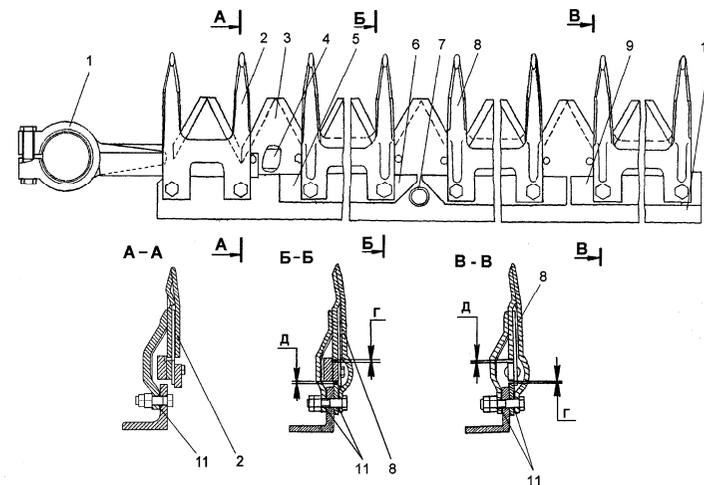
Режущий аппарат: 1 — головка ножа; 2, 8 — пальцы сдвоенные; 3 — сегмент; 4 — полоса ножевая; 5, 6, 9 — пластины трения; 7 — заглушка; 10 — уголок; 11 — прокладки регулировочные
